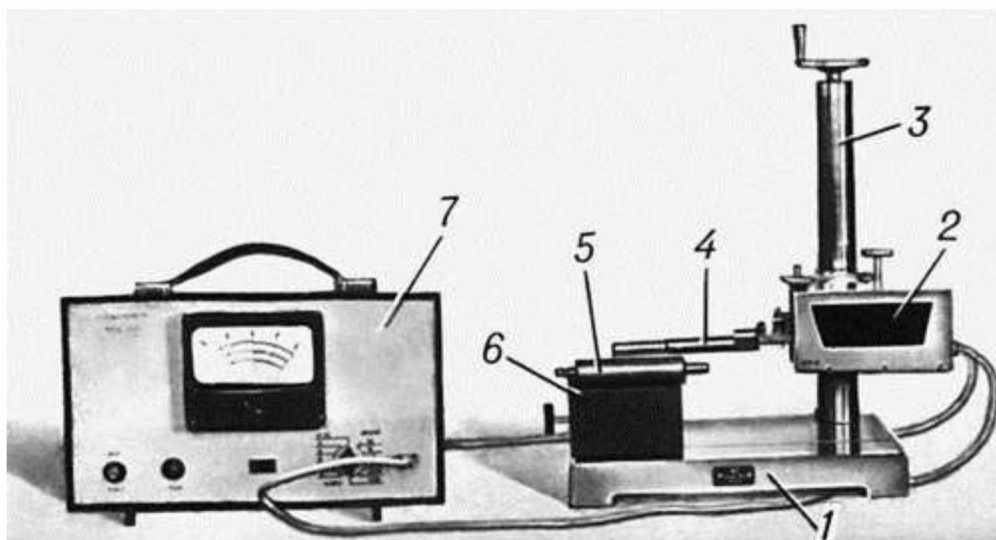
Профілометр (модель 253 заводу «Калібр»): 1 — станина; 2 — привід; 3 — стойка; 4 — датчик; 5 — деталь; 6 — вимірювальний стіл; 7 — електронний блок з показуючим пристроєм.
